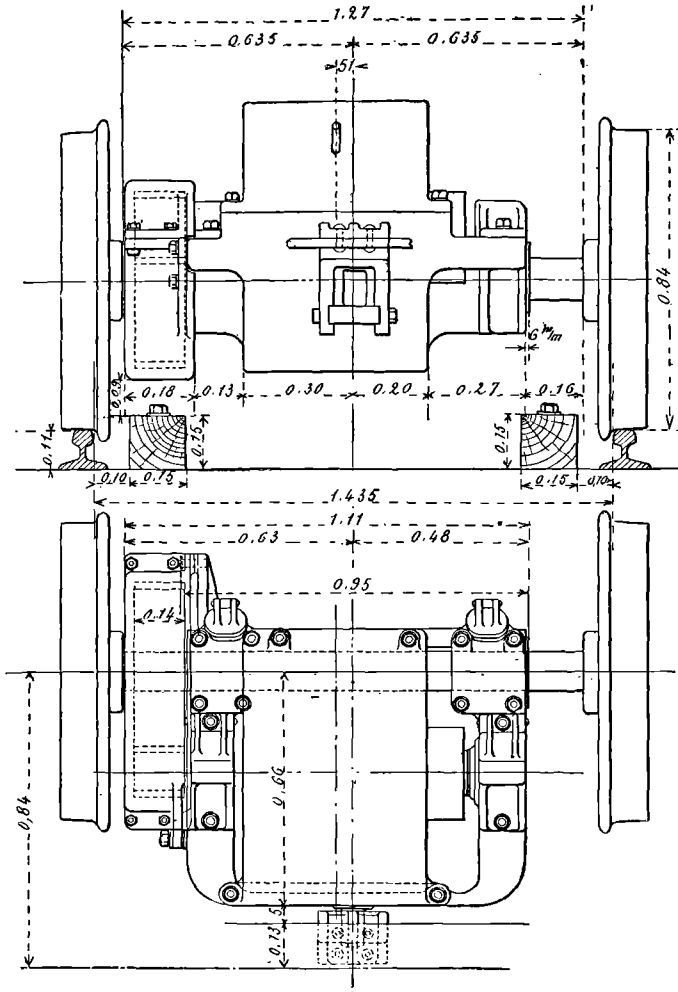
Moteur Walker n° 25 pour métropolitains. — Elévation et plan.
